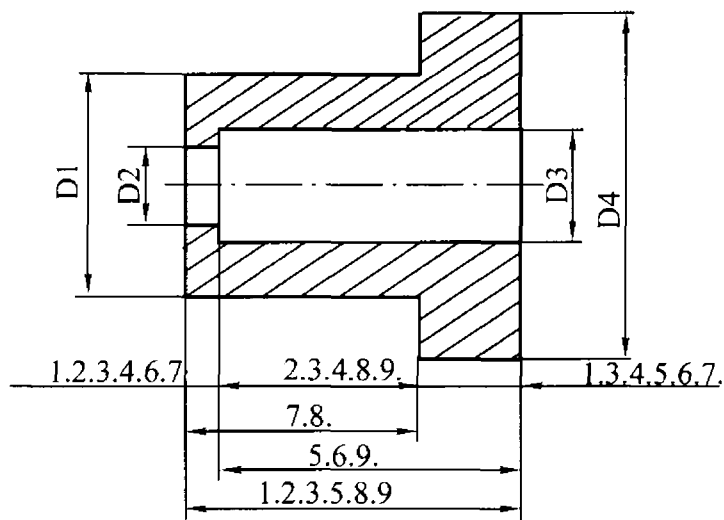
Креслення деталі "стакан" з різними варіантами проставляння розмірів [33].
